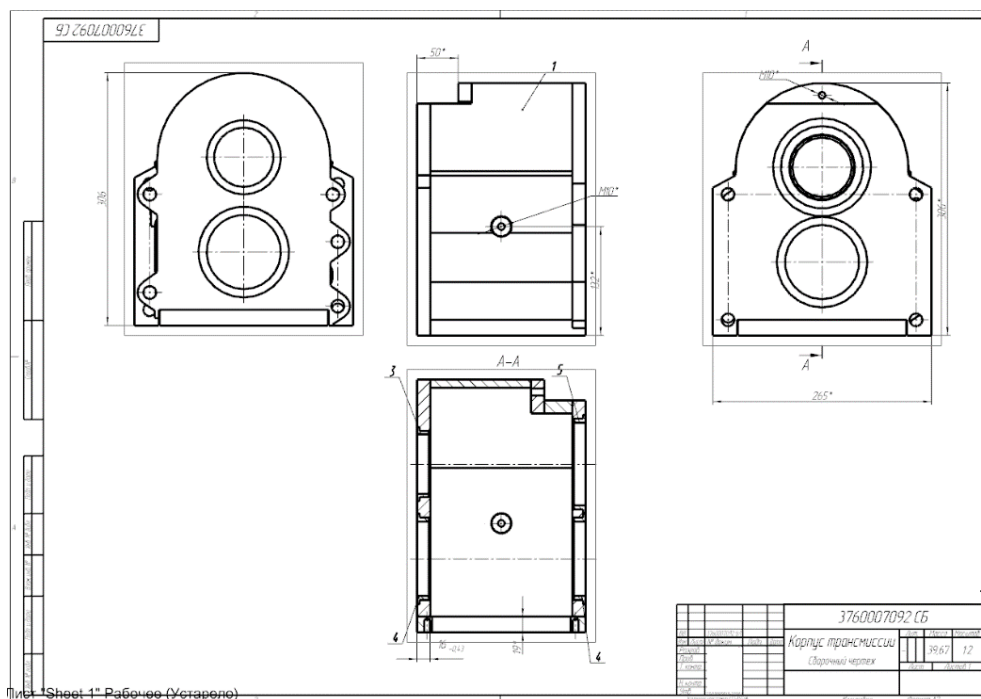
Сборочный чертеж «Корпус коробки передач»
